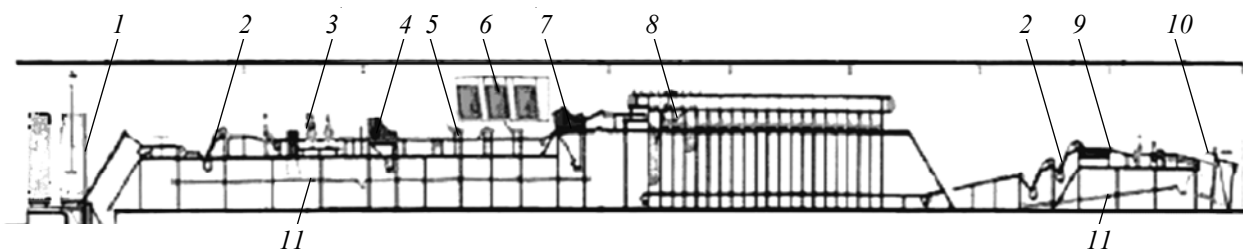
Установка для торцовки, сортировки по длине, маркировки
